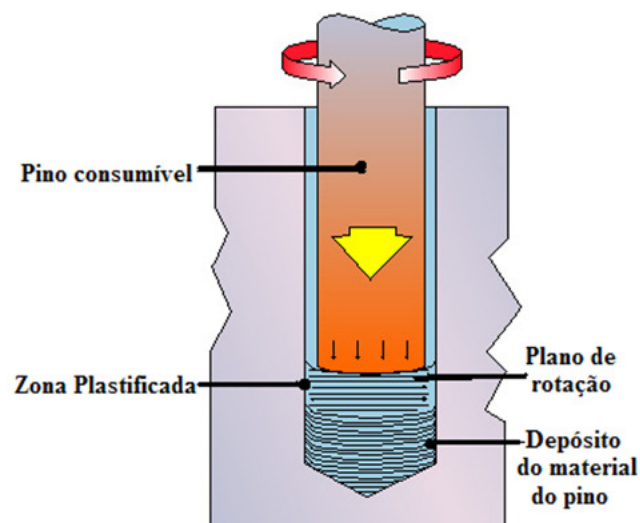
Regiões da soldagem por fricção por pino consumível<sup>(36)</sup>.
